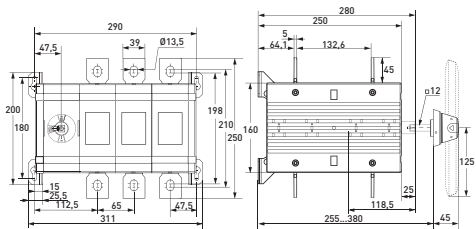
Габаритные и установочные размеры реверсивных рубильников 630-800 А 3Р
